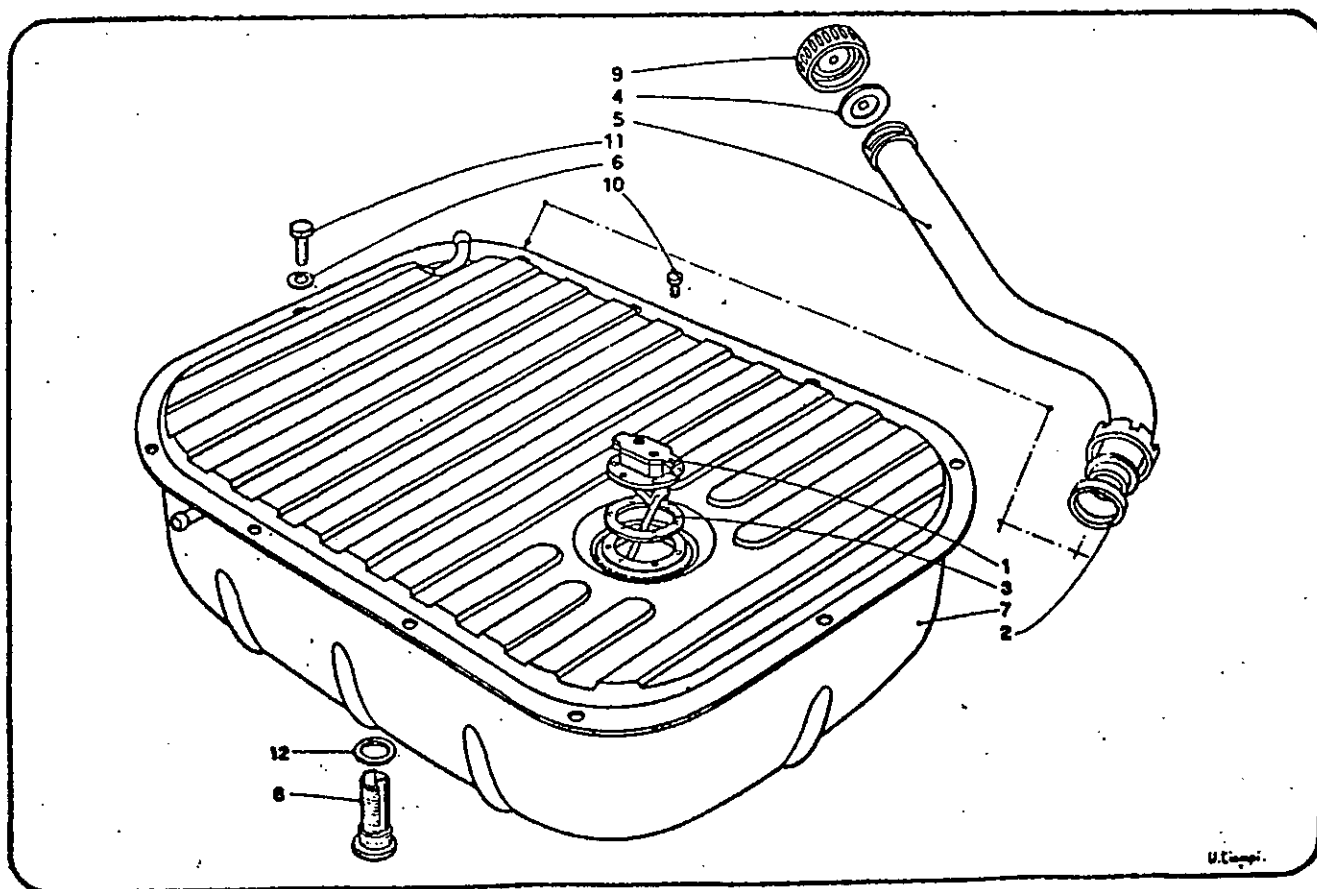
/44 - Réservoir à carburant (du Catalogue Pièces Détachées).
